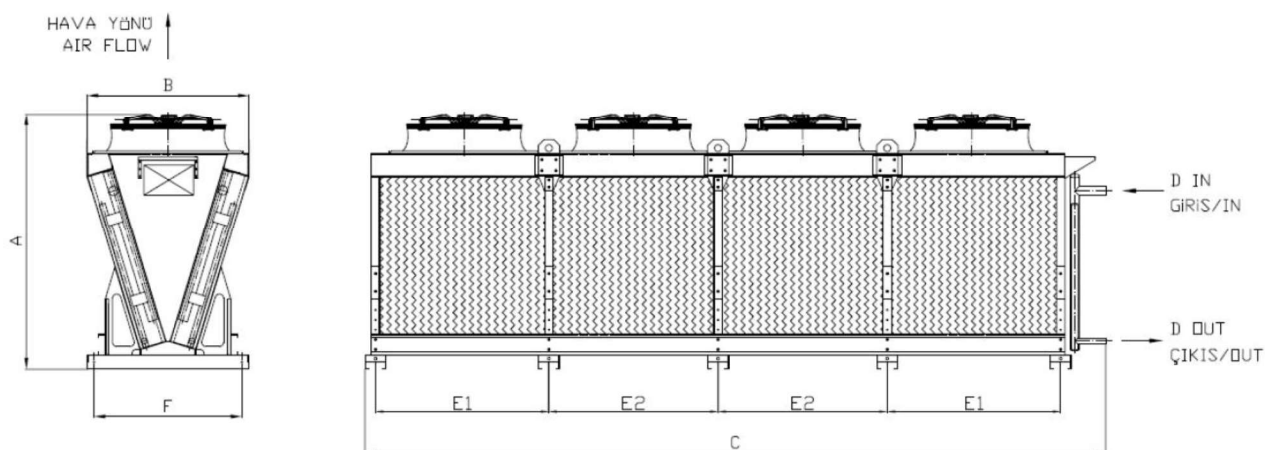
Габаритные размеры конденсатора КС-t-491FB1-B06 C2
